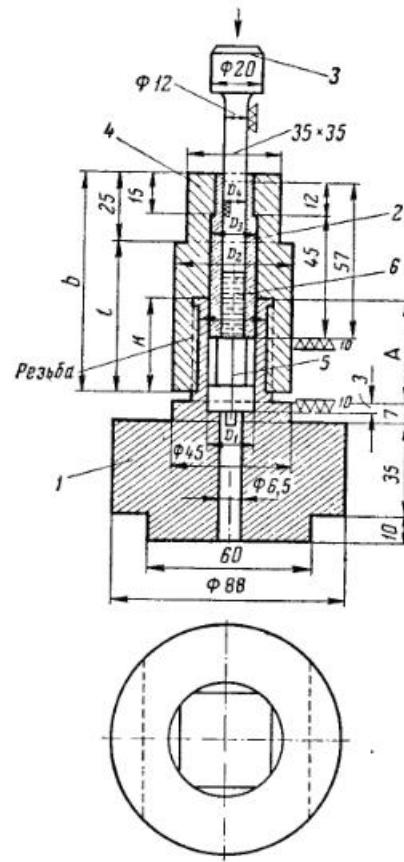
Приспособление для выпрессовки зависших игл форсунок:
